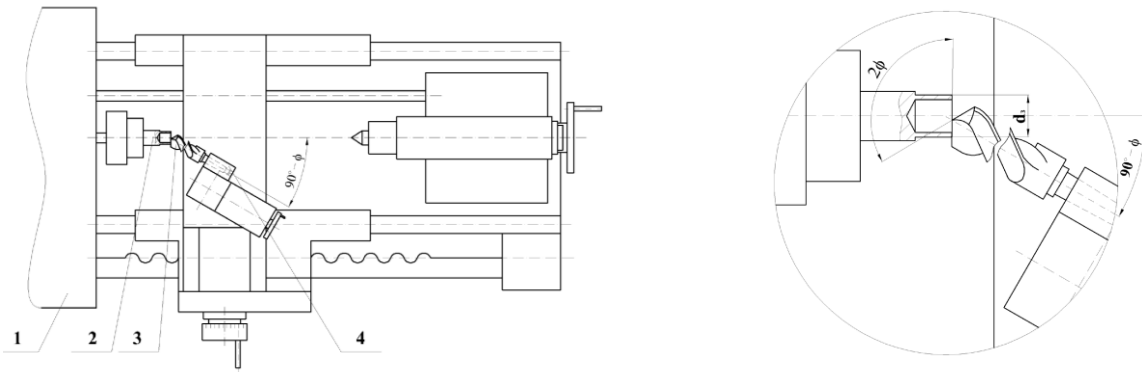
Схема дослідної установки: 1 – токарно-гвинторізний верстат; 2 – оброблюваний дослідний зразок, закріплений в трьохкулачковому патроні; 3 – циліндричне спіральне свердло; 4 – спеціальний тримач для закріплення свердла.
